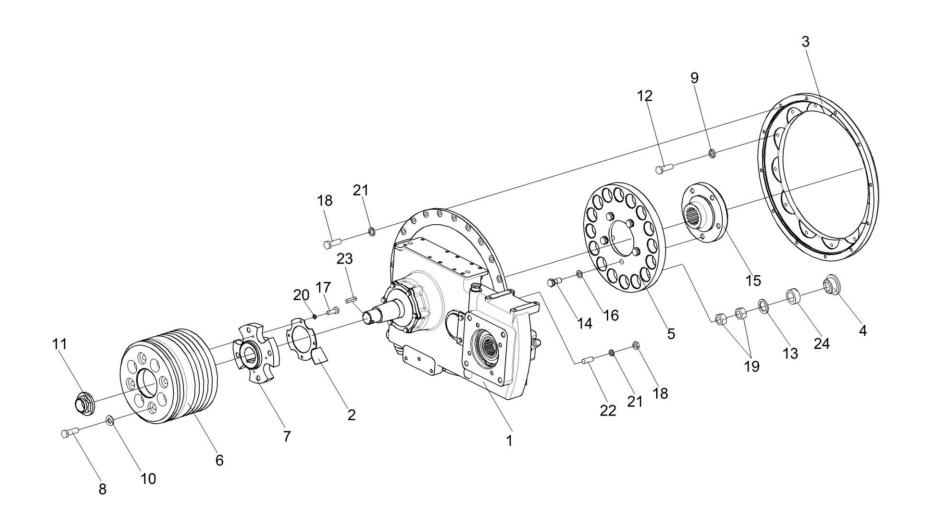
Установка главного привода КЗК-10-1-0106030-01
